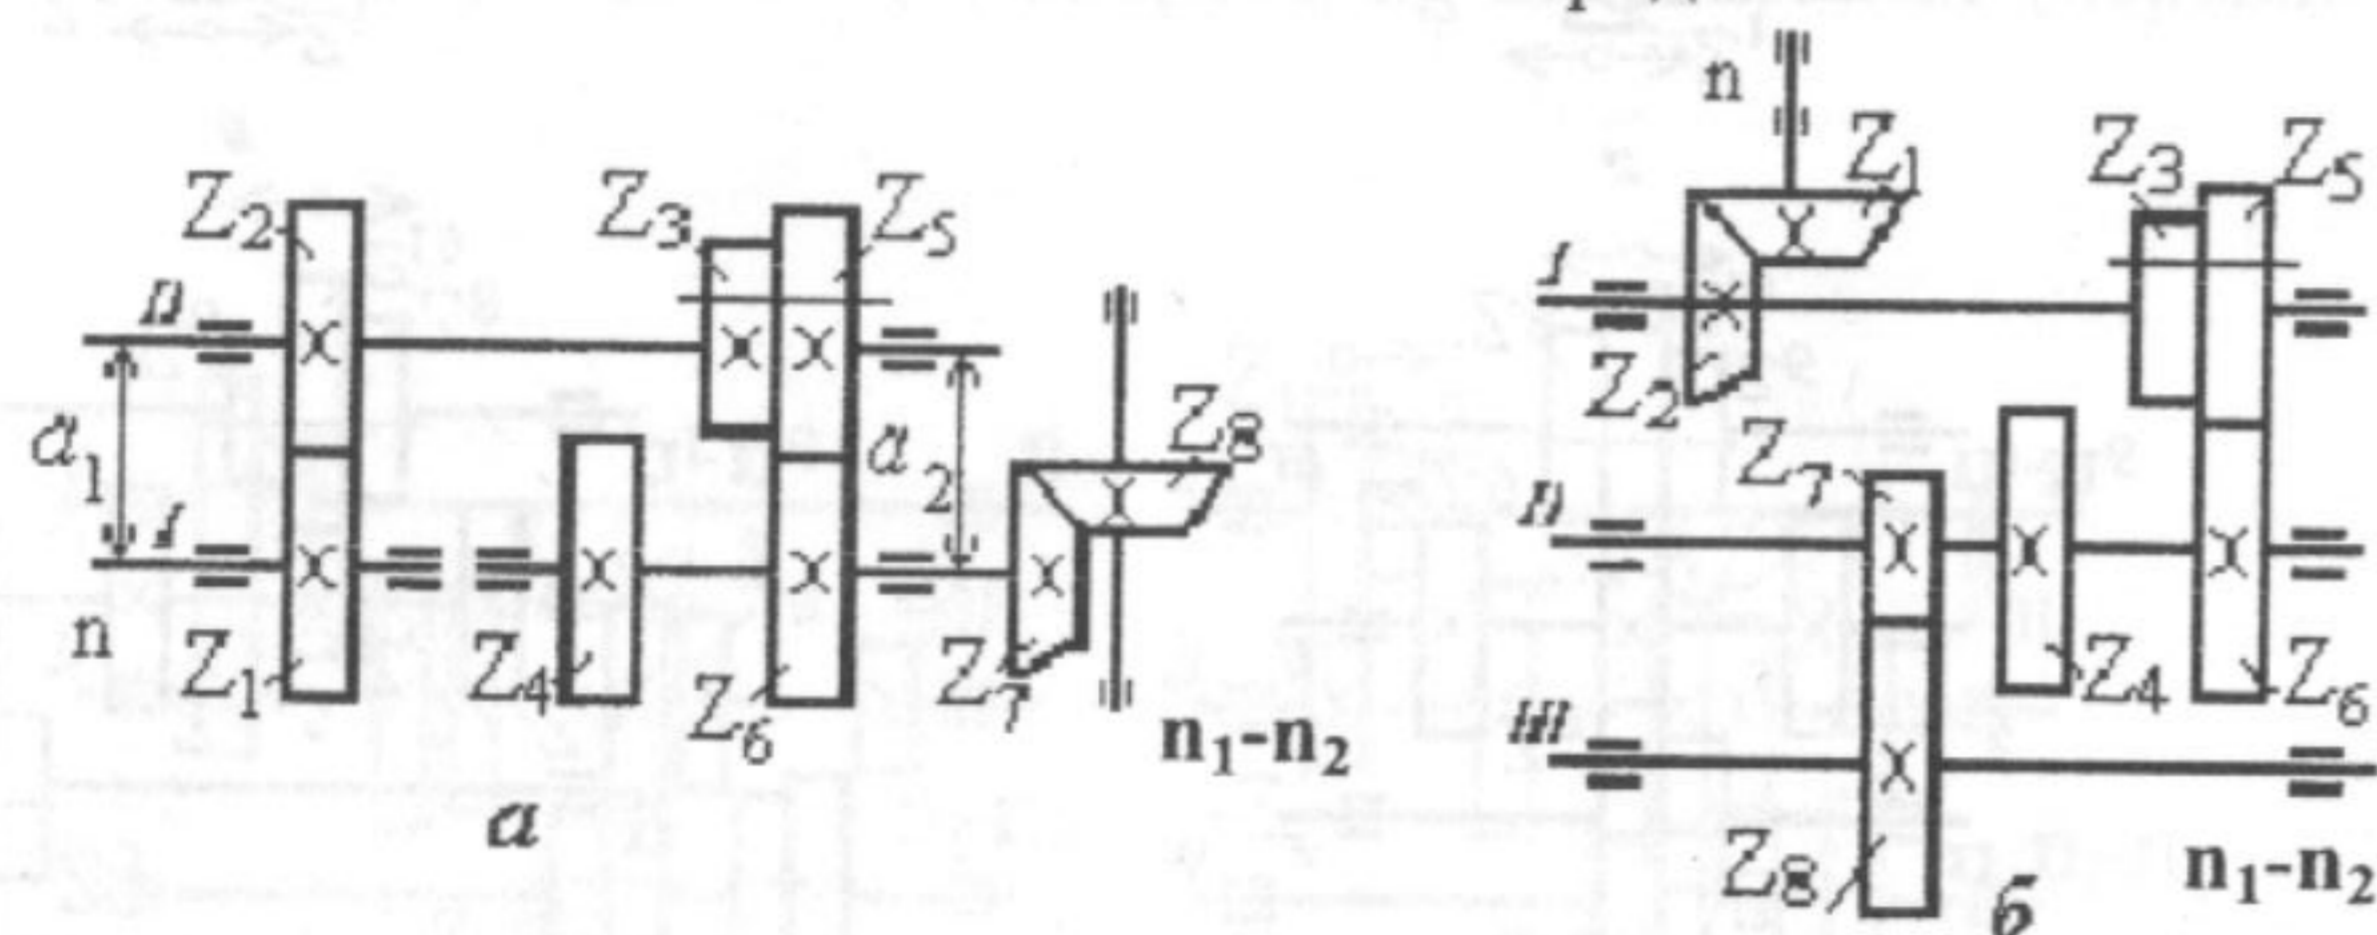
Схемы коробки скоростей с дополнительными цилиндрической и конической передачами
